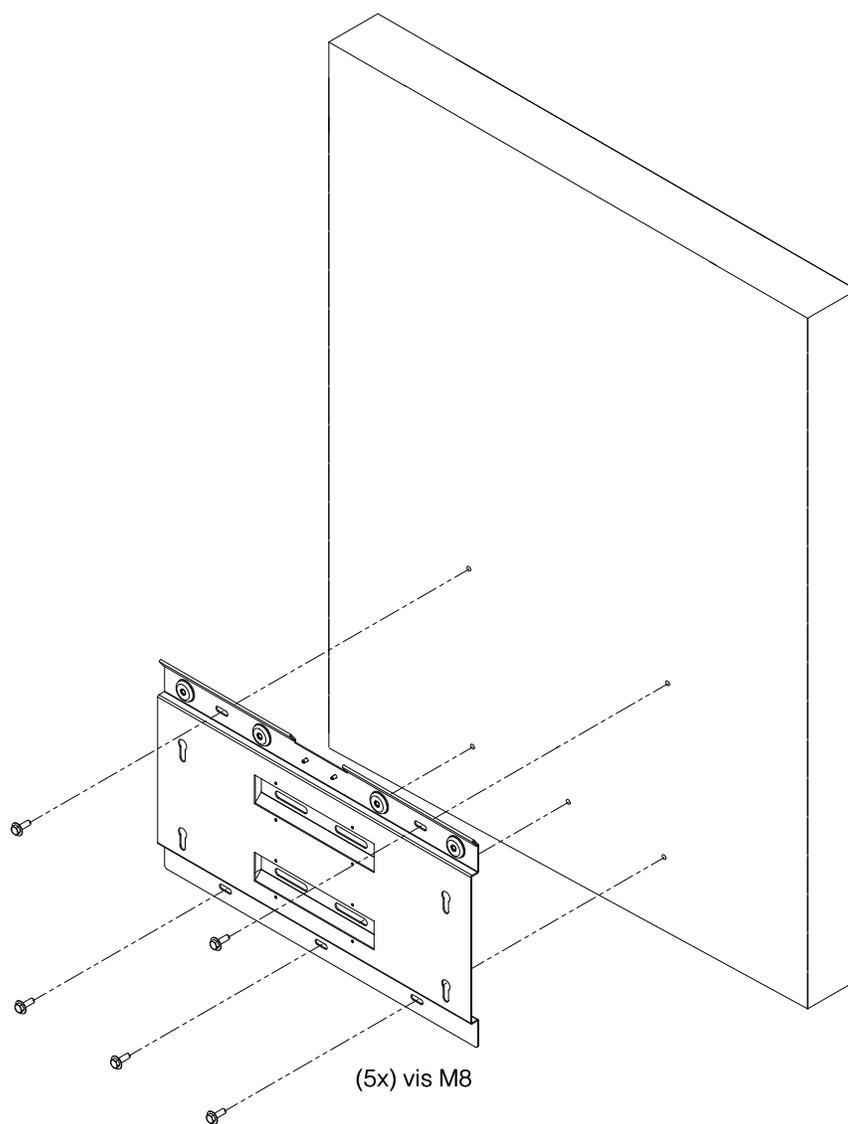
Fixation au mur du support de montage du boîtier de câblage
